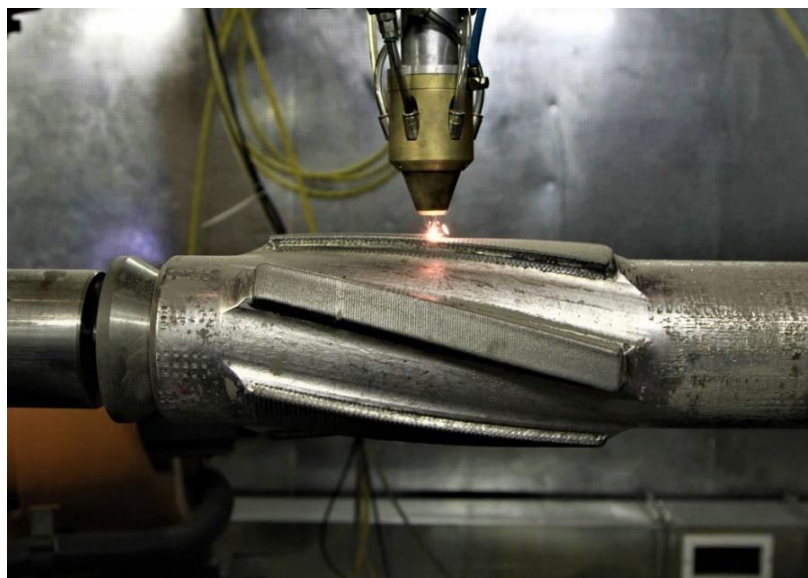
Плазменная наплавка и сварка детали
